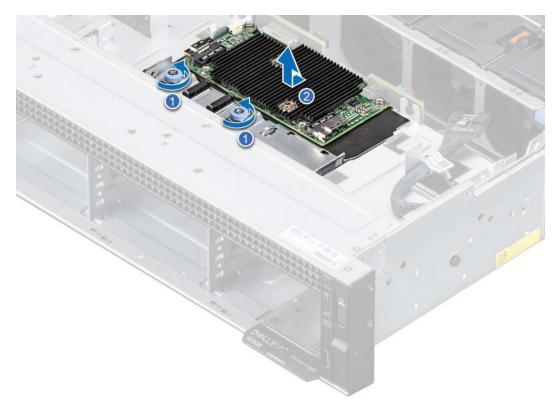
Extracción del módulo de PERC frontal de montaje frontal
